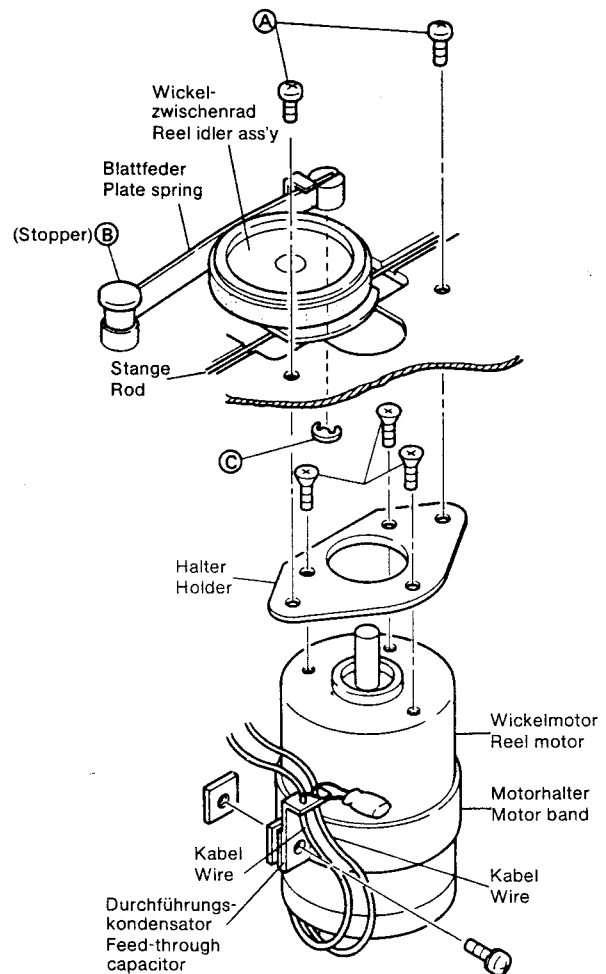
Wickelmotor und Wickelzwischenrad
